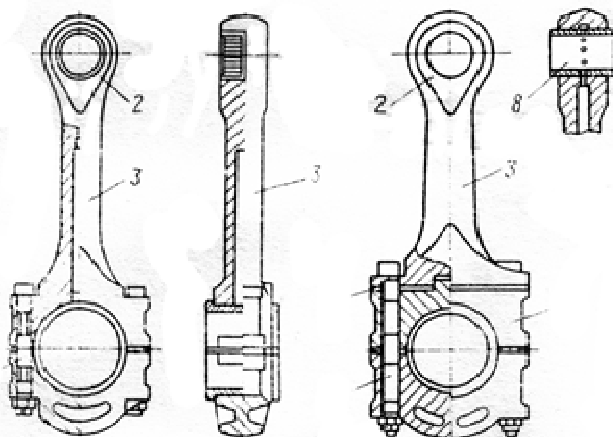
Конструкція шатунів з від'ємною нижньою головкою: 1 – шатунний болт; 2 – верхня головка шатуна; 3 – стрижень шатуна; 4 – вкладиші підшипника нижньої головки шатуна; 5 – прокладка; 6 – нижня головка шатуна; 7 – підшипник (втулка) верхньої головки шатуна
